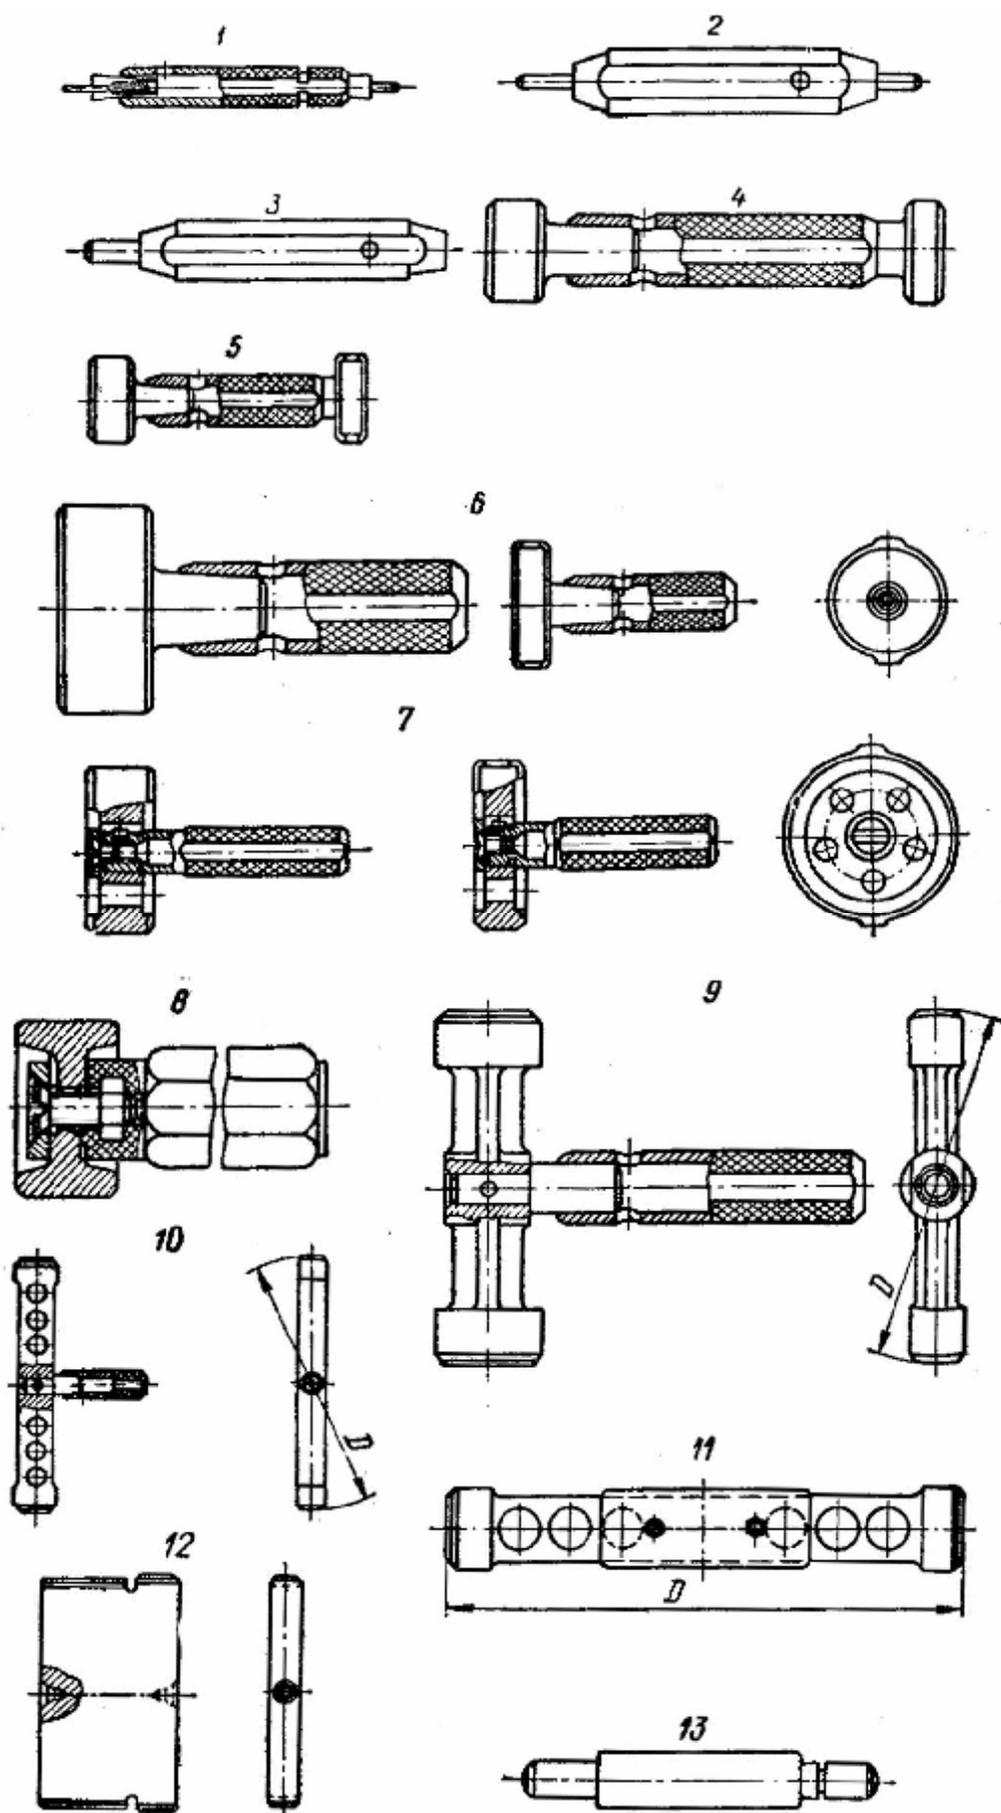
Конструкция и типы калибров для контроля размеров внутренних цилиндрических поверхностей
